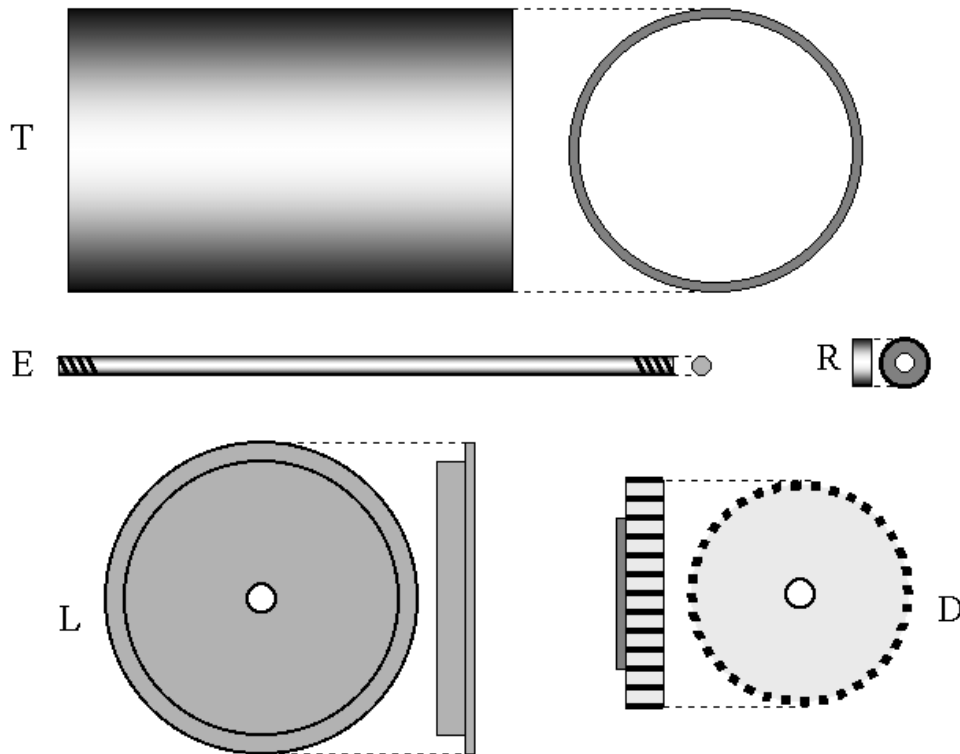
La realización de un registrador de tambor se inicia construyendo el tambor propiamente dicho. Ya que de sus dimensiones finales dependen todas las otras piezas. Tambor, tapa, eje, rodamiento, polea dentada. T tambor, L tapa lateral, E eje, R rodamiento, D polea (dentada).
